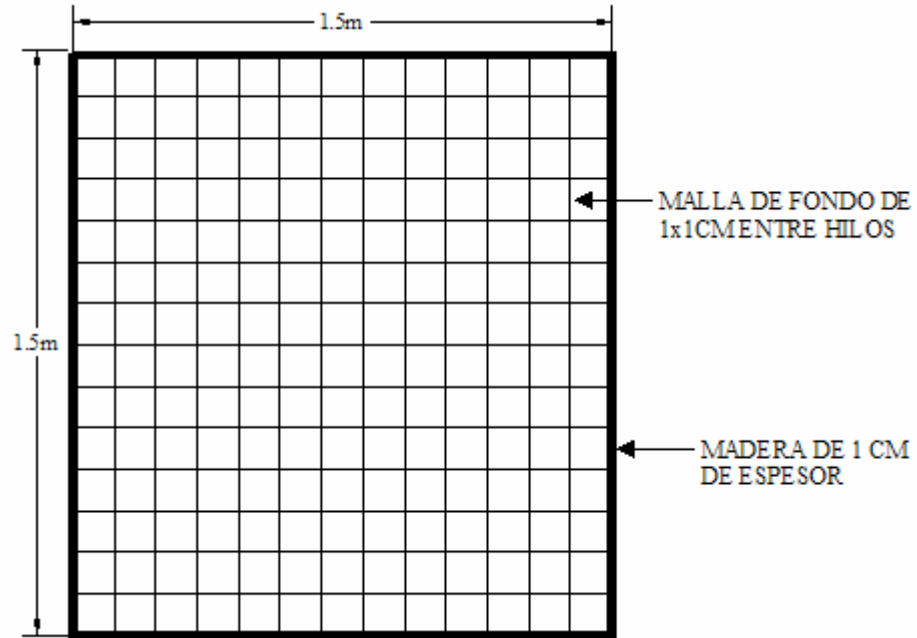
Vista en planta del cajón y la malla de fondo de 1 x 1cm entre hilos
